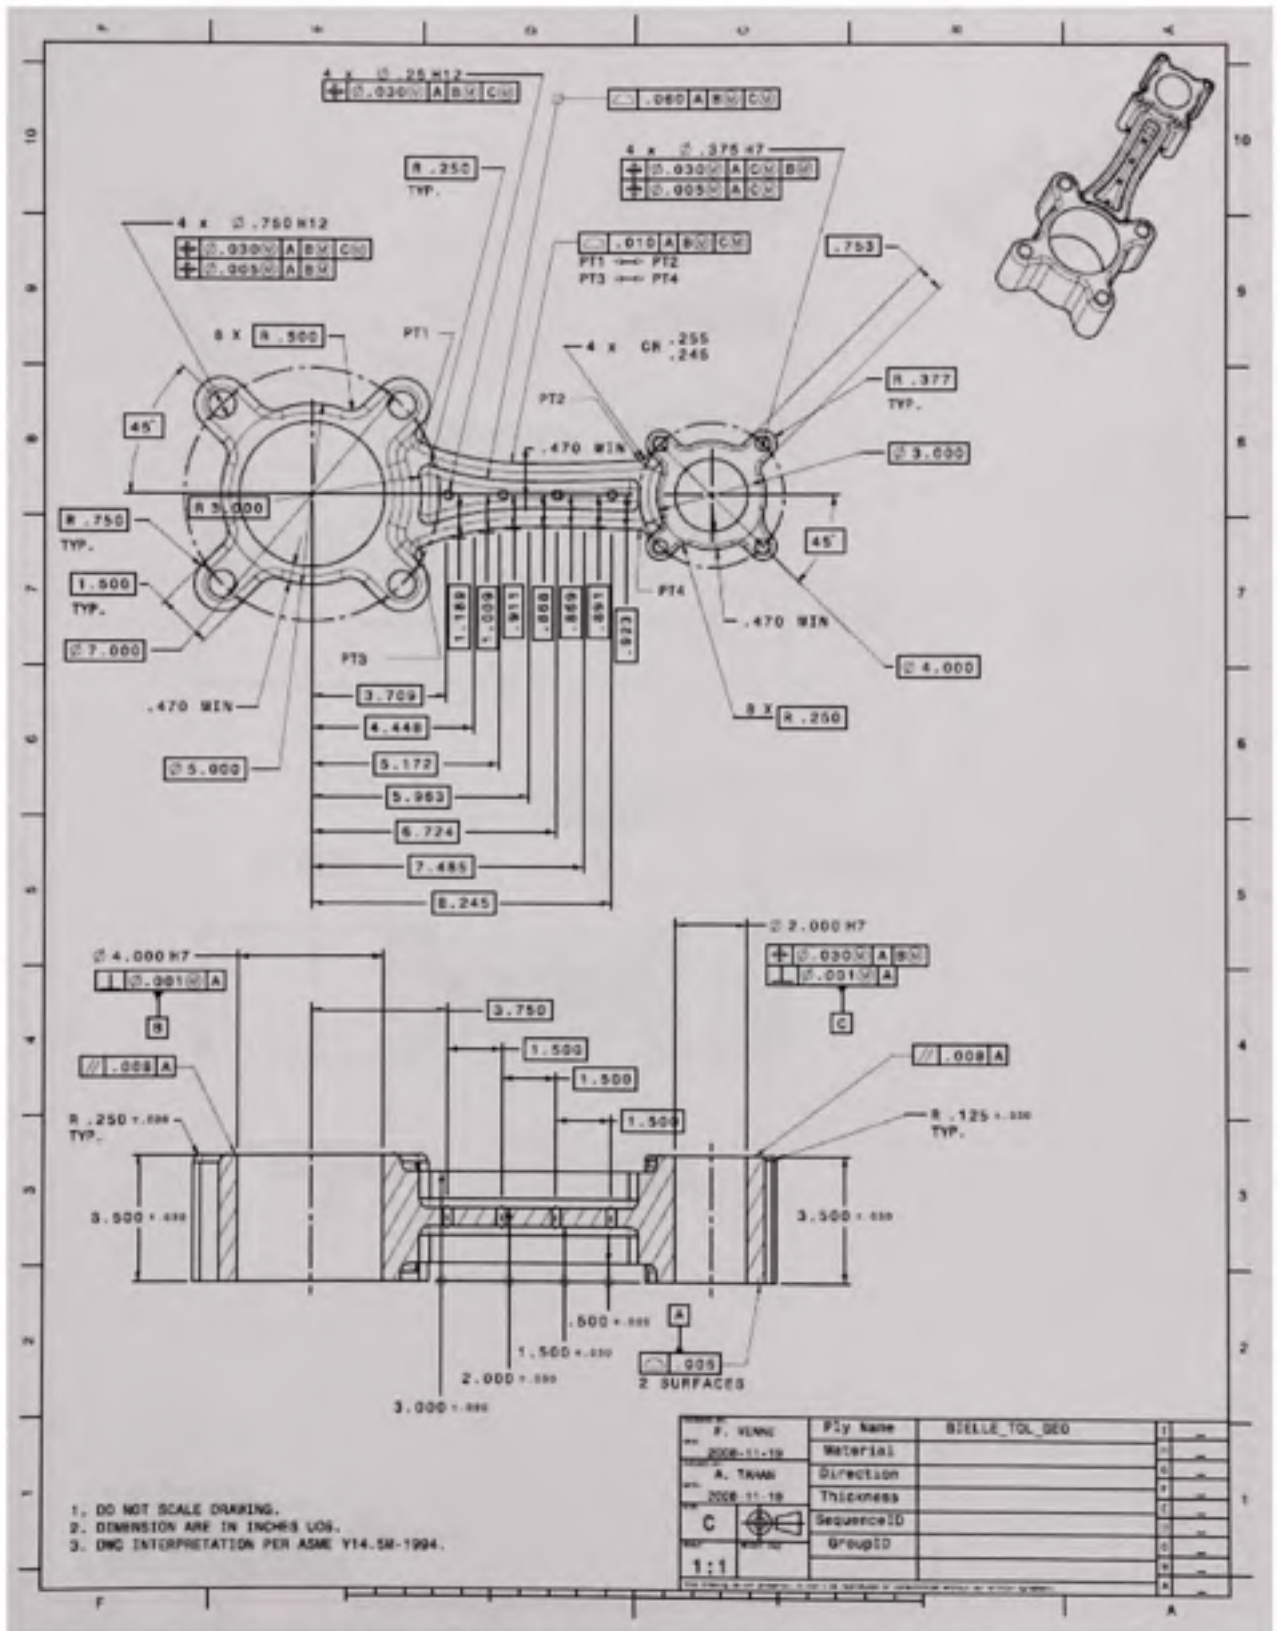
Dessin dimensionnement traditionnel géométrique.
